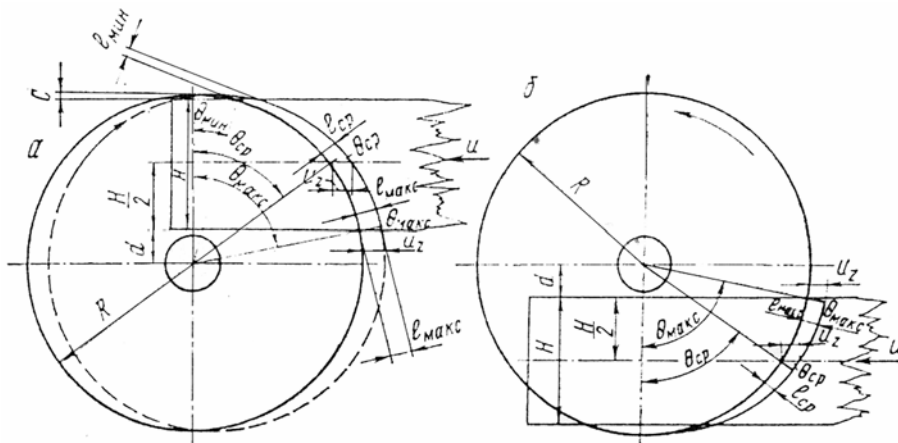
Схема образования стружки при пилении древесины круглыми пилами с расположением пильного вала: а – нижним; б – верхним
